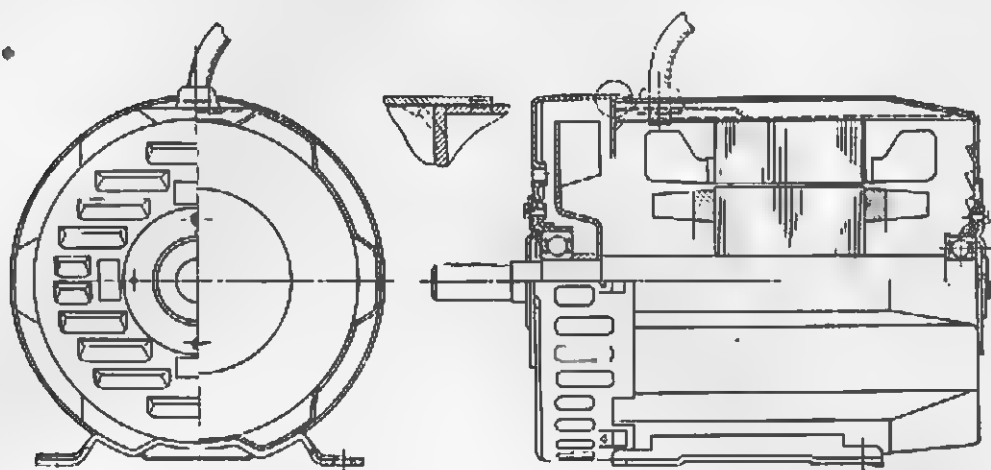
Асинхронный двигатель неразборной конструкции фирмы «Триге-Титан».
